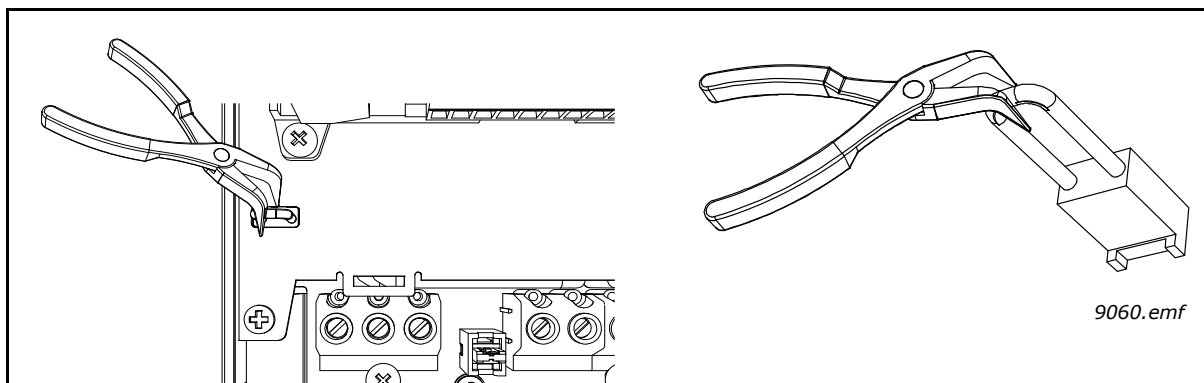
Entfernen der Steckbrücke am Beispiel MR5
